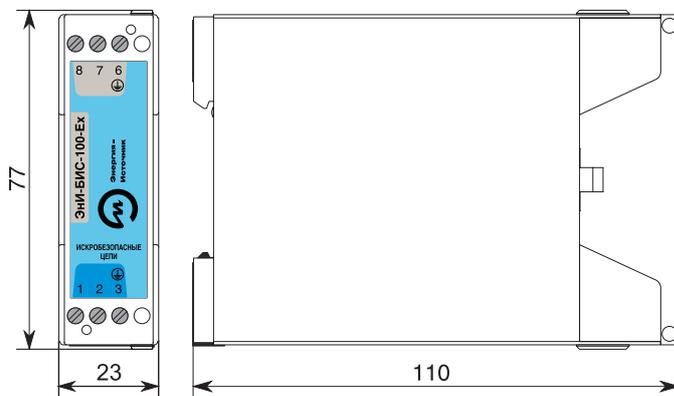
Габаритные размеры барьеров ЭНИ-БИС-101, 102, 105, 109, 111-Ex
